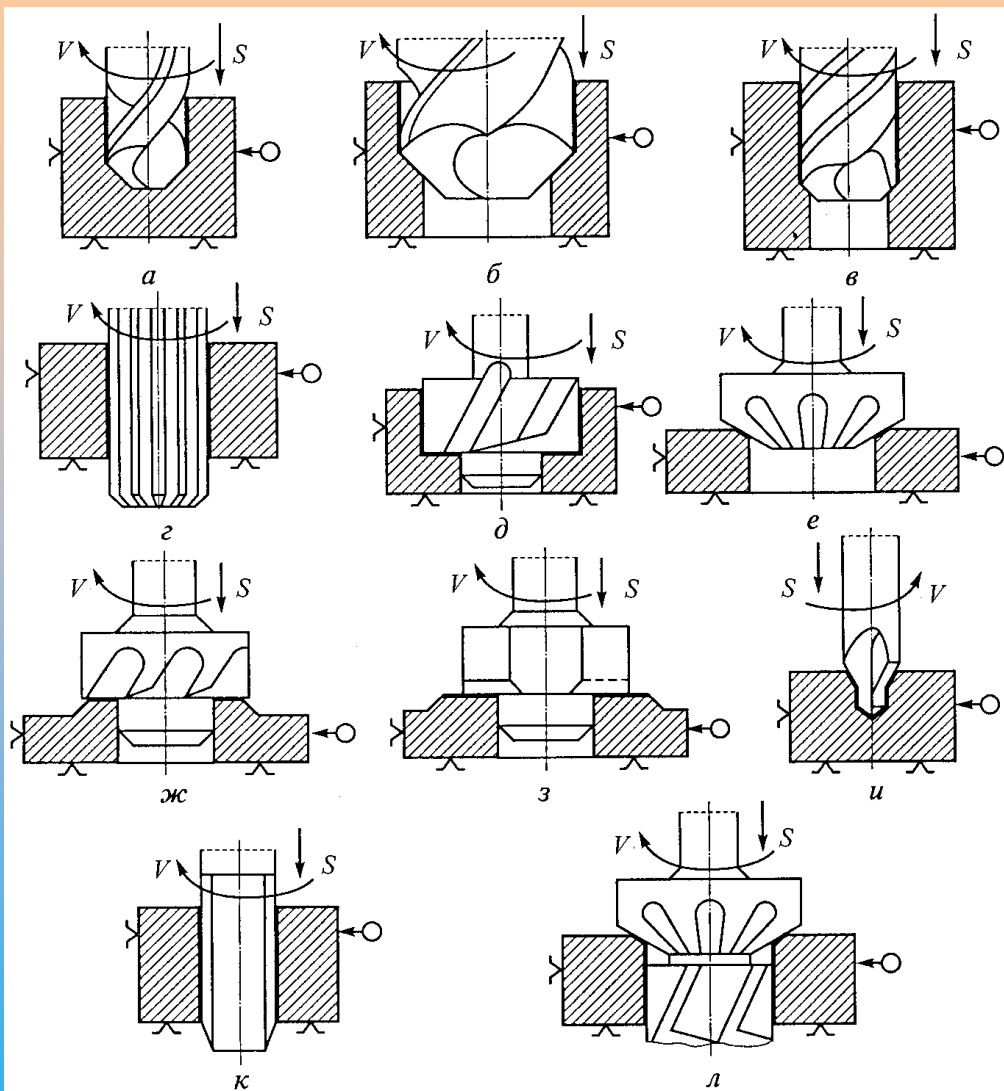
Схемы сверления (а) и рассверливания (б)
